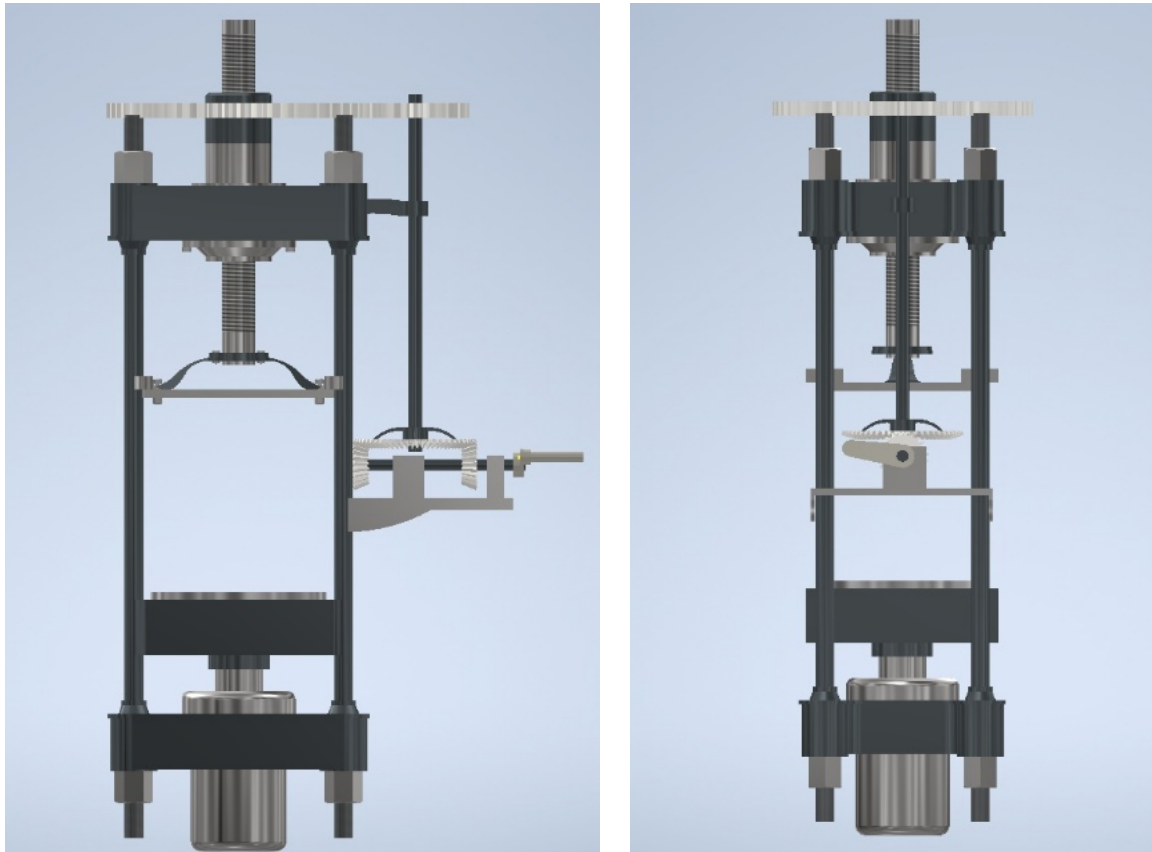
Vistas frontal y lateral del ensamblaje final.
